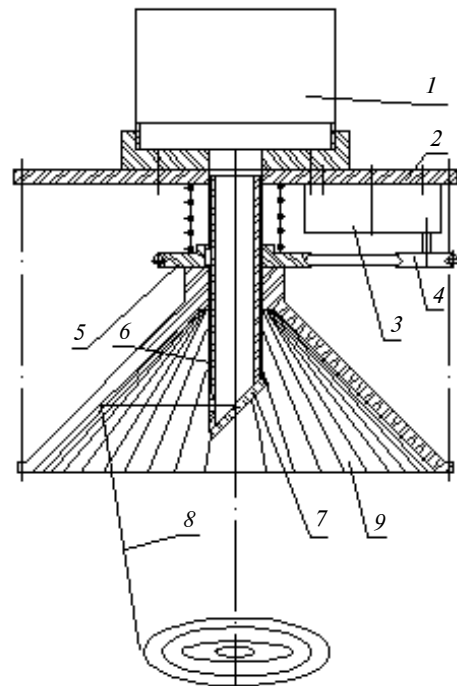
Пристрій для сканування променя вздовж спіралі: 1 – двигун; 2 – корпус; 3 – двигун; 4, 5 – ремінна передача; 6 – різьбова втулка; 7 – поворотне дзеркало; 8 – промінь; 9 – дзеркальний конус
